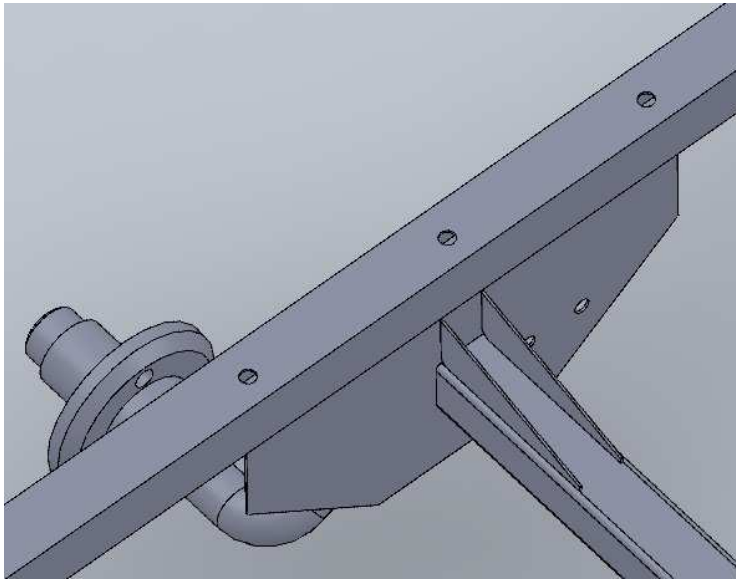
Konstrukční návrh přívěsu – varianta 1. Detailní pohled na spojení tažného kloubu s přírubou a U profilů. Zřetelně jsou vidět otvory pro šrouby.
